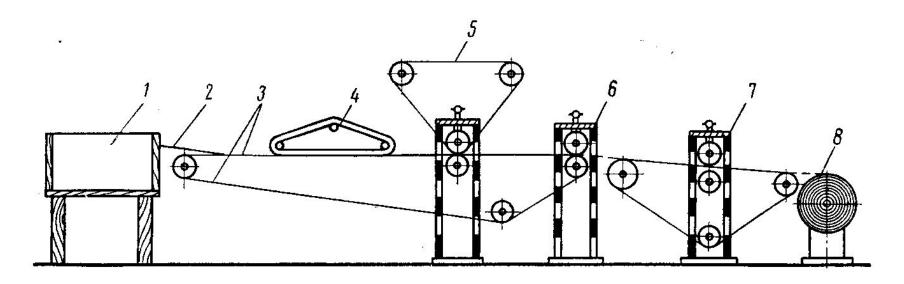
Первая бумагоделательная машина Донкина: 1— черпальный чан; 2— лоток; 3— сетка; 4— декельный ремень; 5— гауч-пресс; 6 и 7— прессы; 8— накат
